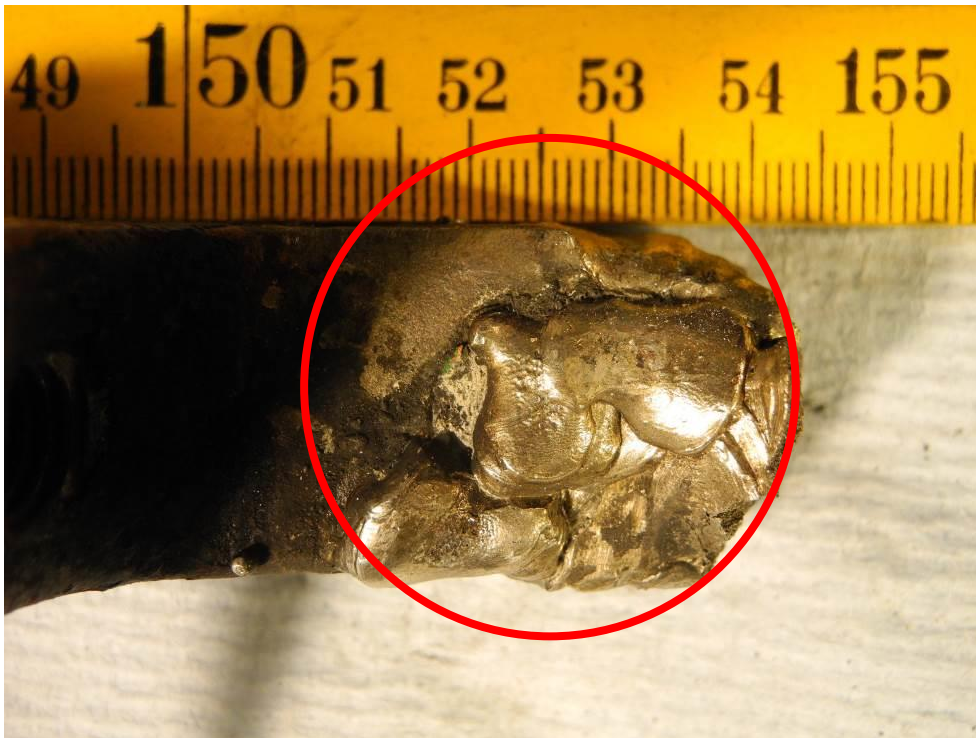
Makroaufnahme der Schweißung mit Lunker und Einbrandkerben
